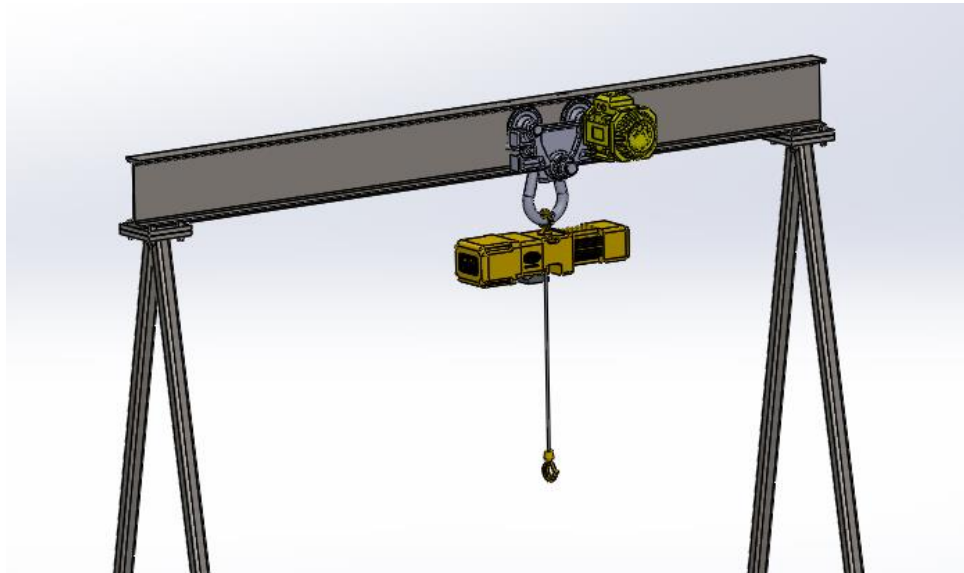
Ensamble Trolley y polipasto.* Fuente: Autor
